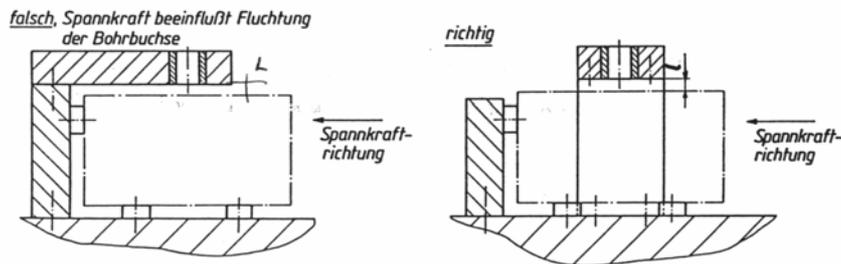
Einbau einer Bohrbuchse l – Abstand der Bohrbuchse zur Werkstückkante
